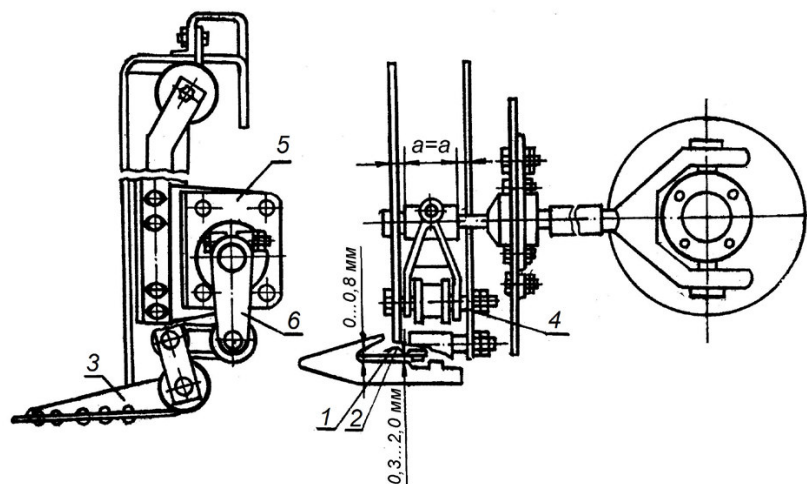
Схема привода режущего аппарата: 1 – сегмент; 2 – прижим; 3 – головка ножа; 4 – подвеска привода; 5 – плита шарнира; 6 – приводной балансир
